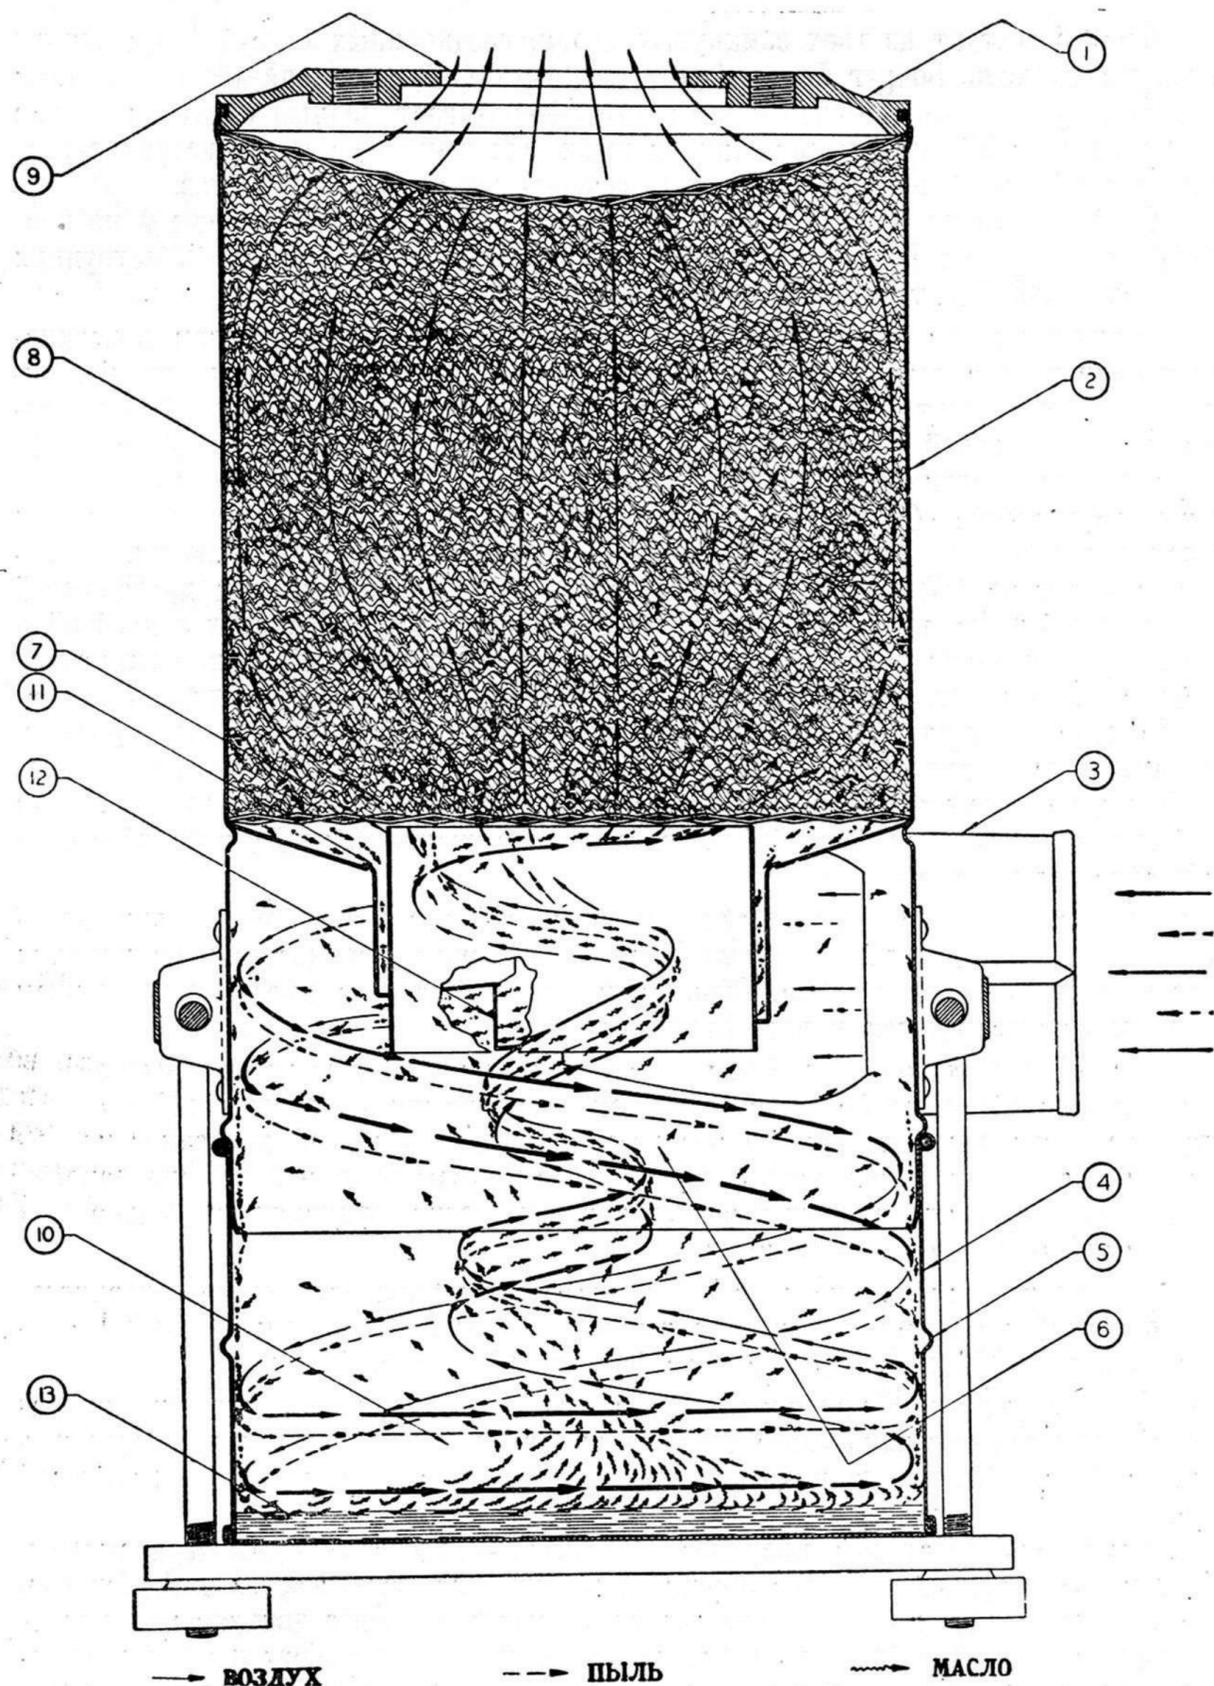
Воздухоочиститель Вортокс. 1 — флянец воздухоочистителя; 2 — корпус воздухоочистителя; 3 — входная воздушная труба; 4 — чашка очистителя; 5 — уровень наполнения чашки маслом; 6 — вихревая камера; 7 — внутренний цилиндр перегородки; 8 — проволочный фильтр; 9 — выход воздуха; 10 — масляный резервуар; 11 — возвратная труба; 12 — отверстие возвратной трубы; 13 — осадочные слои.
